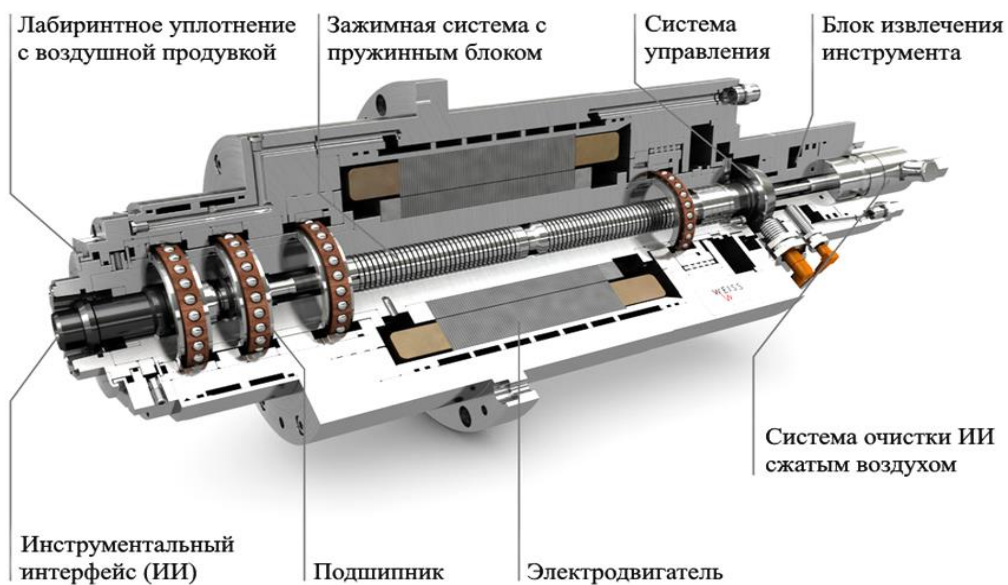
Устройство мотор-шпинделя фрезерного станка с ЧПУ
